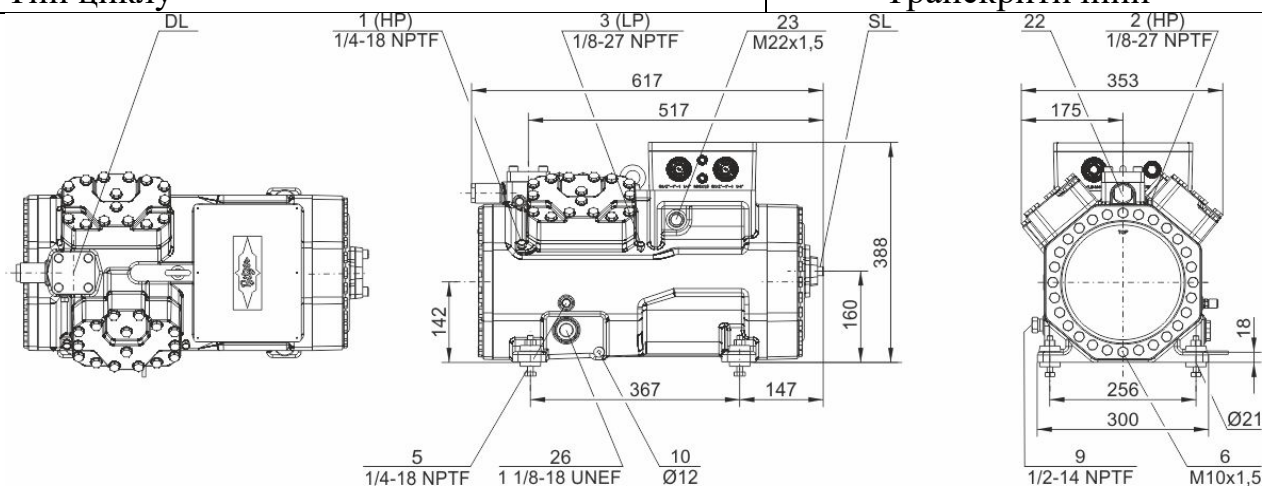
Компрессорный агрегат Bitzer 4JTE-10K-40P.
